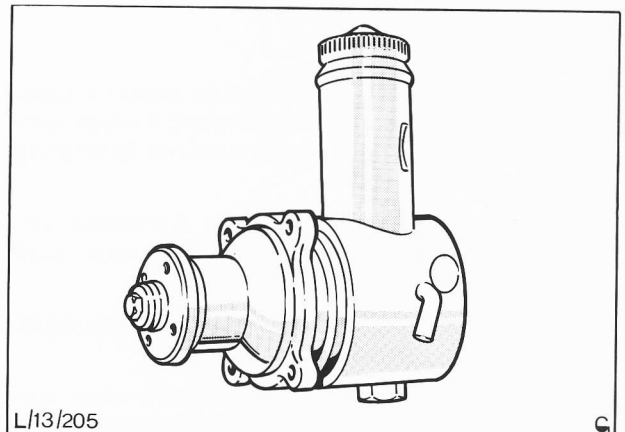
Pumpe mit integriertem Vorratsbehälter
